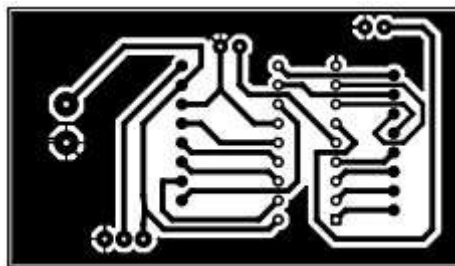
Diseño de las pistas del motor Bipolar para la placa PCB.
